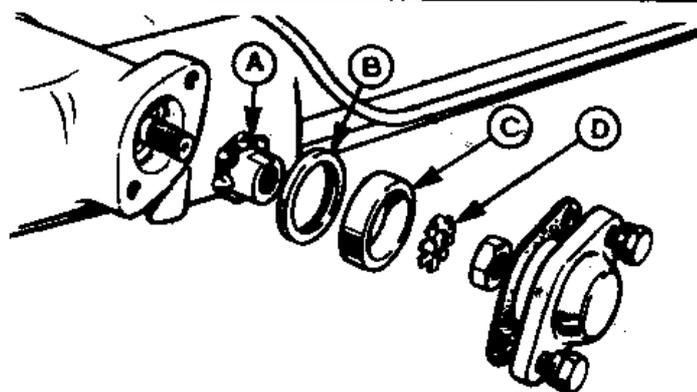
Снятие нижнего подшипника шестерни (Разд.35)
